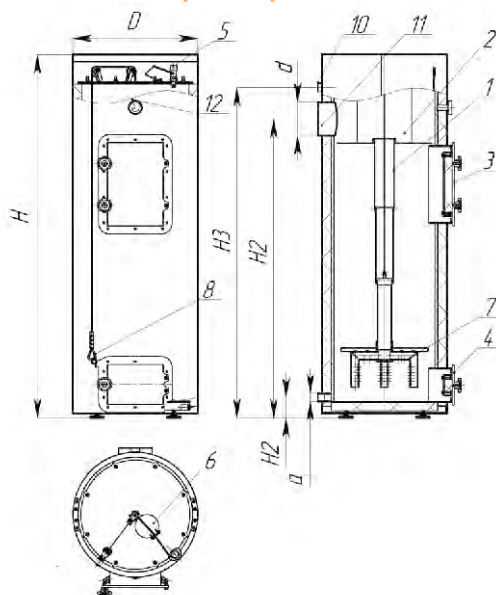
Габаритные и присоединительные размеры версии Comfort-XX (1 – телескопическая труба подачи воздуха, 2 – камера подогрева воздуха, 3 – проем для загрузки дров, 4 – проем для удаления золы, 5 – терморегулятор, 6 – устройство для регулирования подачи воздуха, 7 – распределитель воздуха, 8 – трос, 10 – патрубок подачи воды, 11 – дымоход для отвода дымовых газов, 12 – термоманометр).
